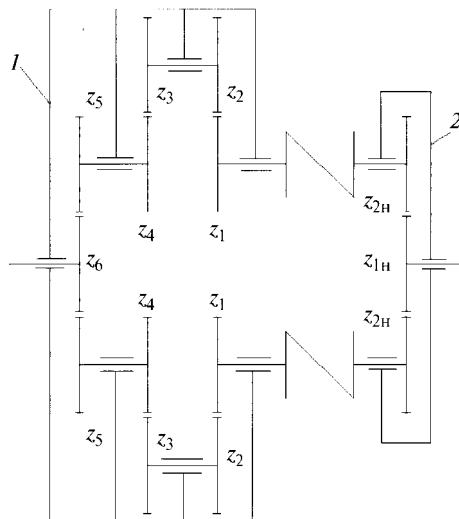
Кинематический контур из валов и зубчатых передач обкатываемого редуктора 1 и механизма нагружения 2
